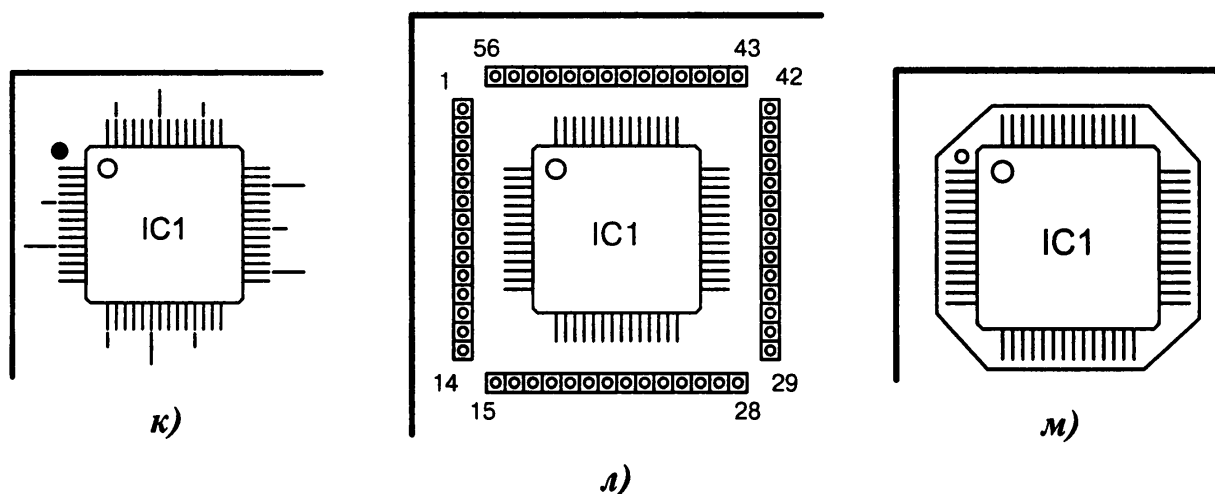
Маркировка микросхем в корпусе TQFP-56 (окончание):
